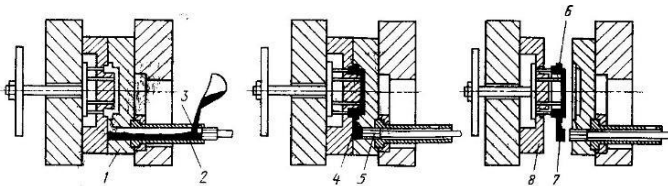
Схема лиття під тиском на машинах з гарячою камерою пресування
